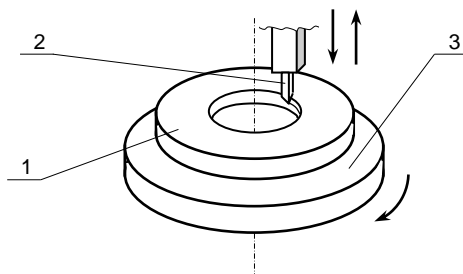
Схема работы токарно-карусельного станка:
